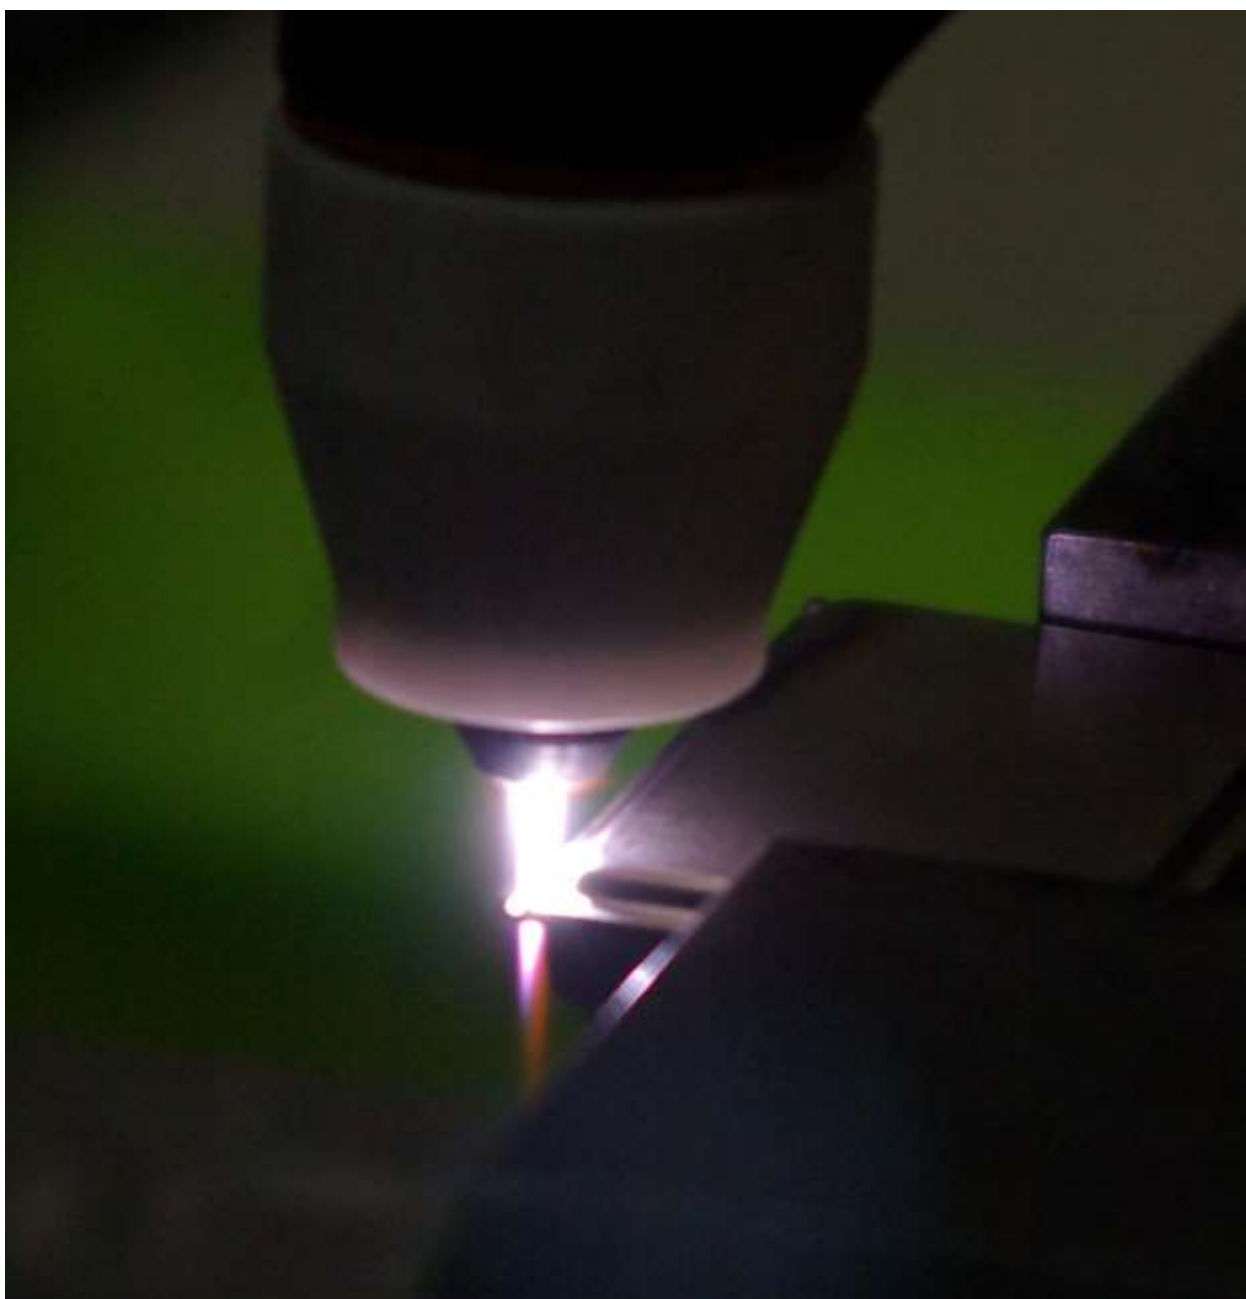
Сварка только с дежурной дугой
